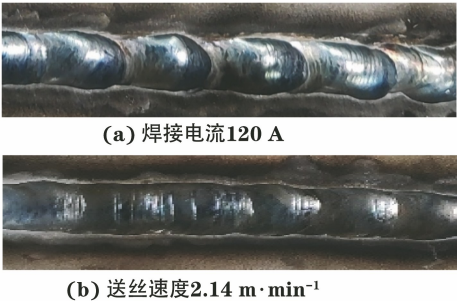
焊接电流 120 A 和送丝速度 2.14 m/min 时的焊缝形貌
